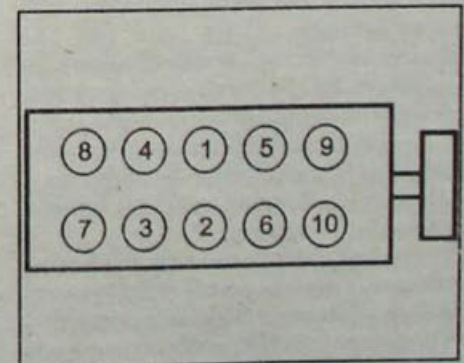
Последовательность затягивания болтов крепления головки цилиндров двигателя F3R
